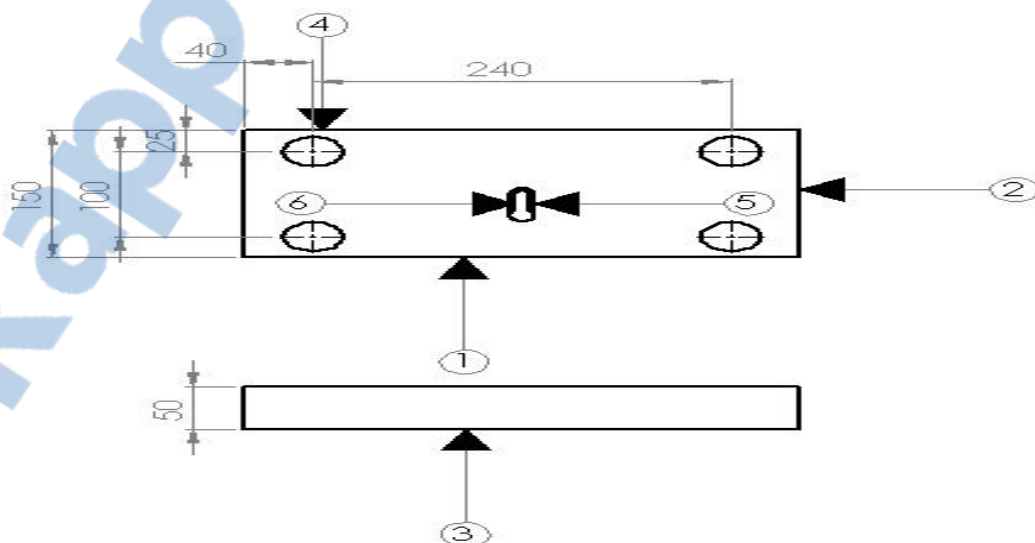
les numérotations de faces de la plaque de fixation d'éprouvette
